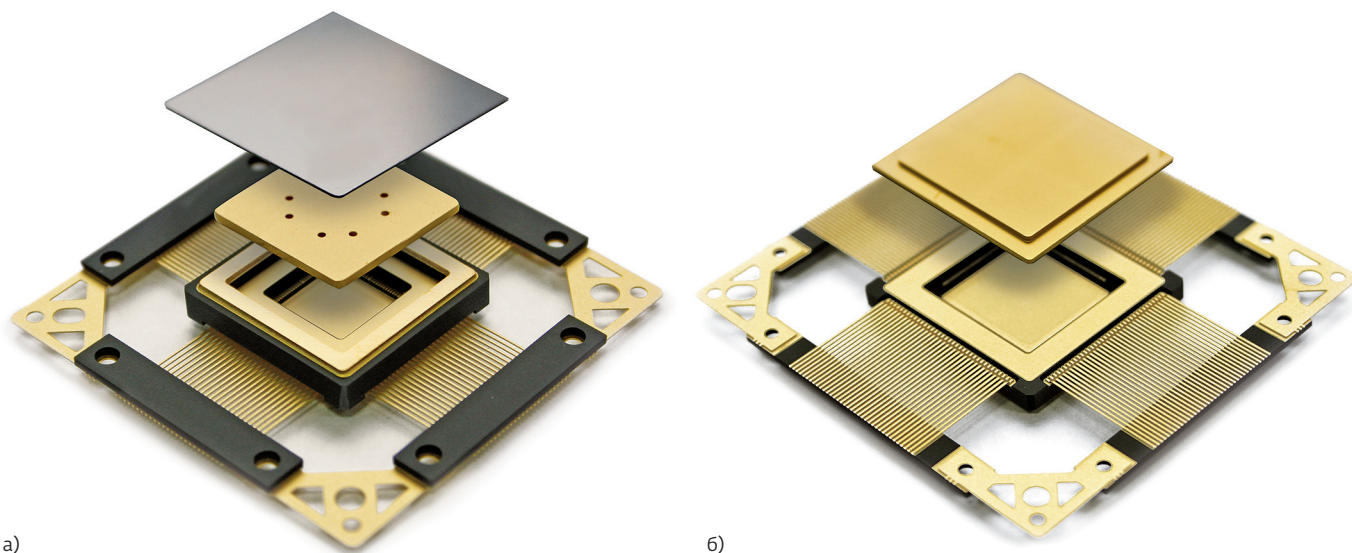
Варианты металлокерамического корпуса с интегрированным ЭРЗ на основе композитного материала W-Si: а) 100-выводной планарный корпус с герметизацией пайкой, б) 144-выводной планарный корпус с герметизацией шовно-роликовой сваркой
